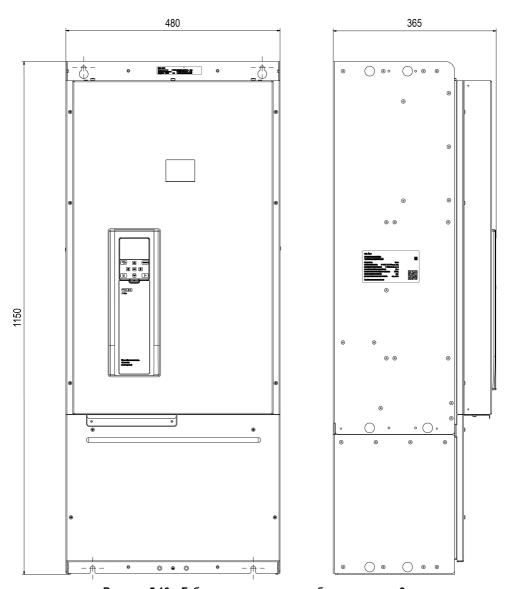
Габаритные размеры прибора в корпусе 6
